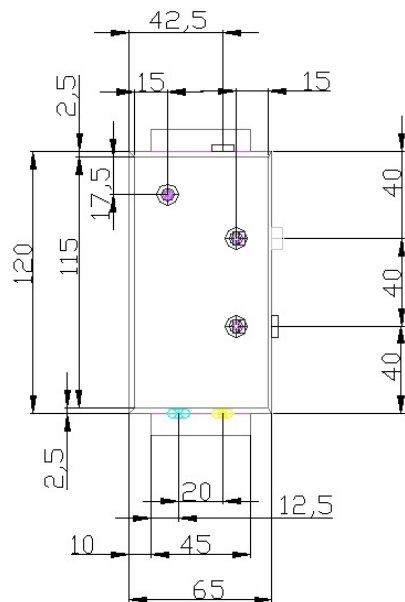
, Grundriss elektrische Steuerung
